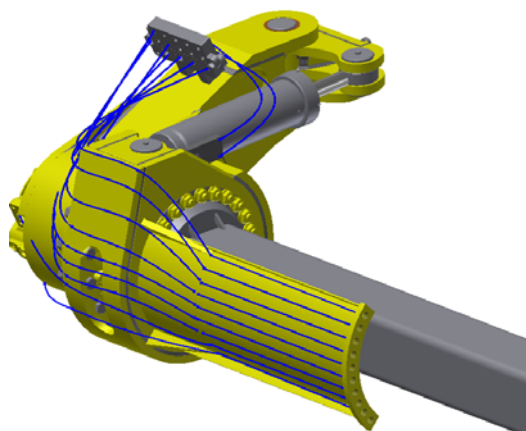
Hydraulikkssystemet med slangepølser langs teleskoparmen
